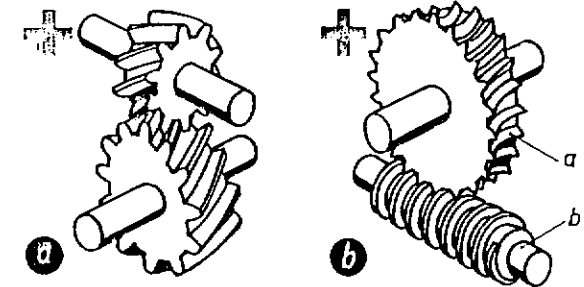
(a) Engranaje de ruedas helicoidales; (b) engranaje de tornillo sin fin. a) rueda helicoidal; b) tornillo sin fin.
